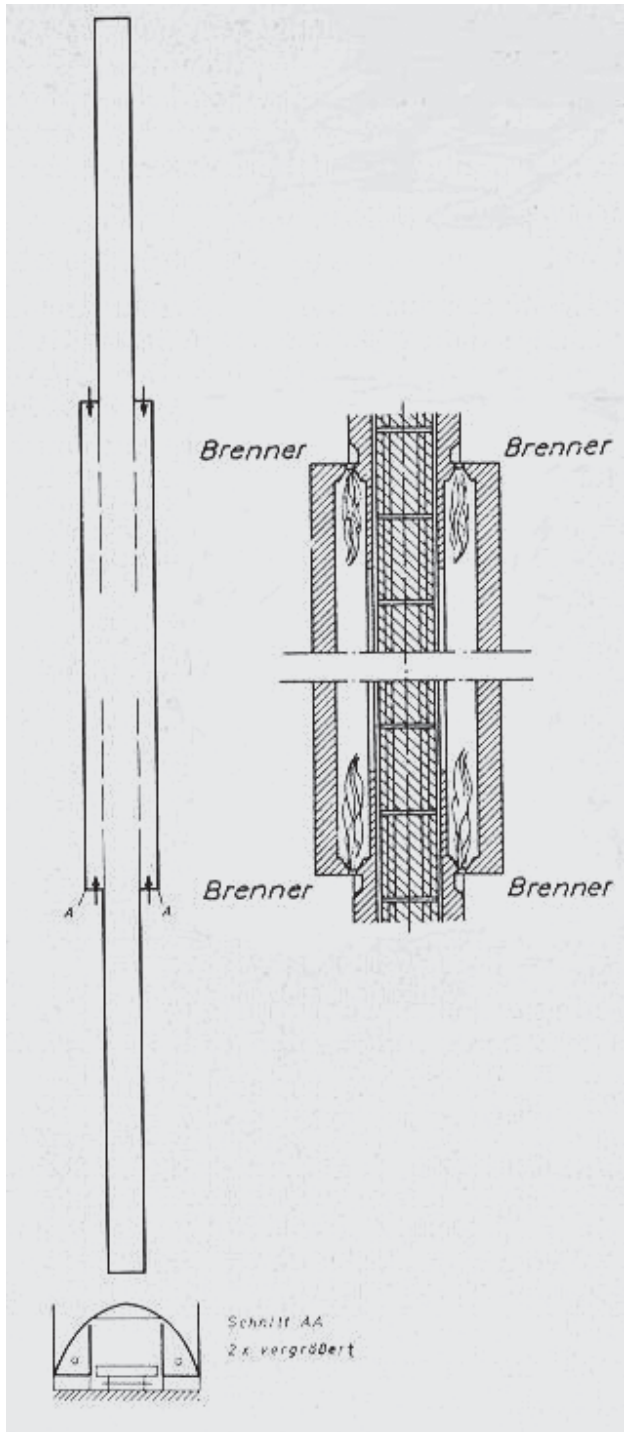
Mac-Aleavy-Tunnelofen, 1950. Diese Öfen wurden zum Teil mit wassergefüllten „Sandrinnen“ betrieben, da Wasser sehr gut abdichtet
